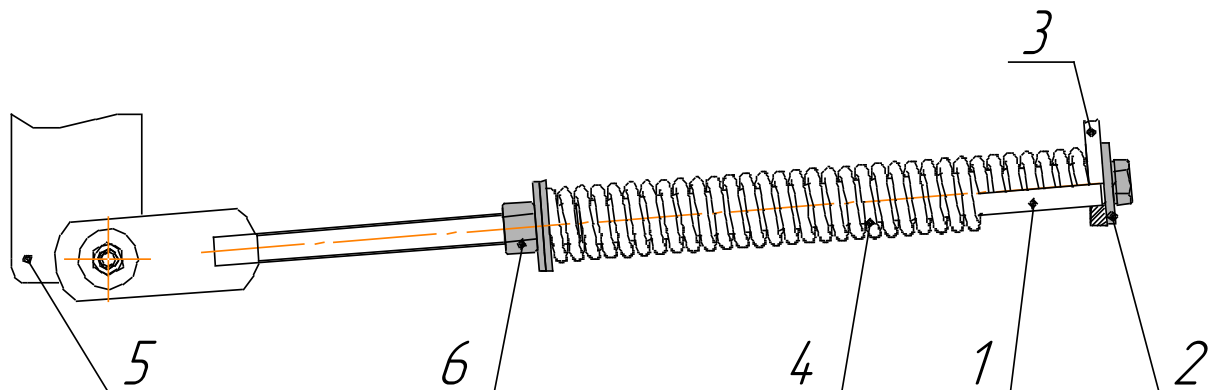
Регулировка пружинного амортизатора подборщика: 1 - направляющая амортизатора; 2 – шайба; 3 – проушина на раме передней камеры; 4 – пружина; 5 – рама подборщика; 6 – гайка;
